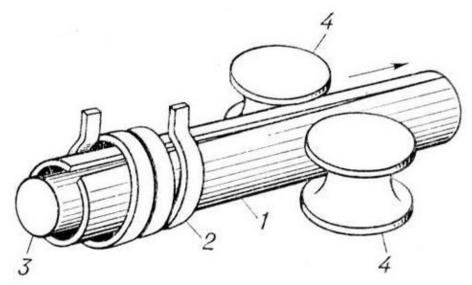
Шовная сварка трубы индукционным способом: 1 – труба; 2 – индуктор; 3 – сердечник; 4 – обжимные ролики.
